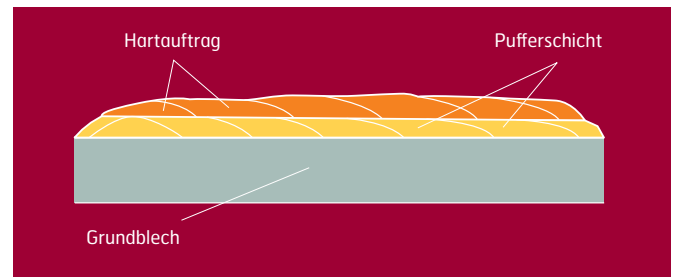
Beispiel für Schweißfolge mit Zusatzwerkstoffen für Pufferschicht und Hartauftrag
